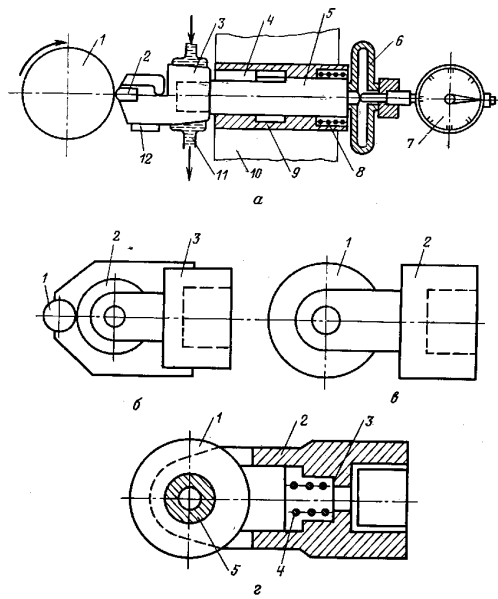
Схема динамометричної оправки (а) зі змінними головками (б, в і г) для зміцнення ЕМО та ППД деталей, відновлених металопокриттями: а- оправлення: 1-деталь; 2 - інструмент; 3 - головка для інструменту; 4 - шпонка; 5 - шток; 6 пружний елемент; 7 -індикатор; 8 - пружина; 9 - втулка корпусу; 10 - супорт верстата; 11 - охолоджуючий кожух; 12 - наконечник струмопроводу; б - кулькова головка: 1 - кулька; 2 - кульковий підшипник; 3 - вилка головки; в і г - роликові головки: 1 - ролик; 2 -вилка головки; 3 - мідно-графітова щітка; 4 - пружина; 5-вісь ролика
